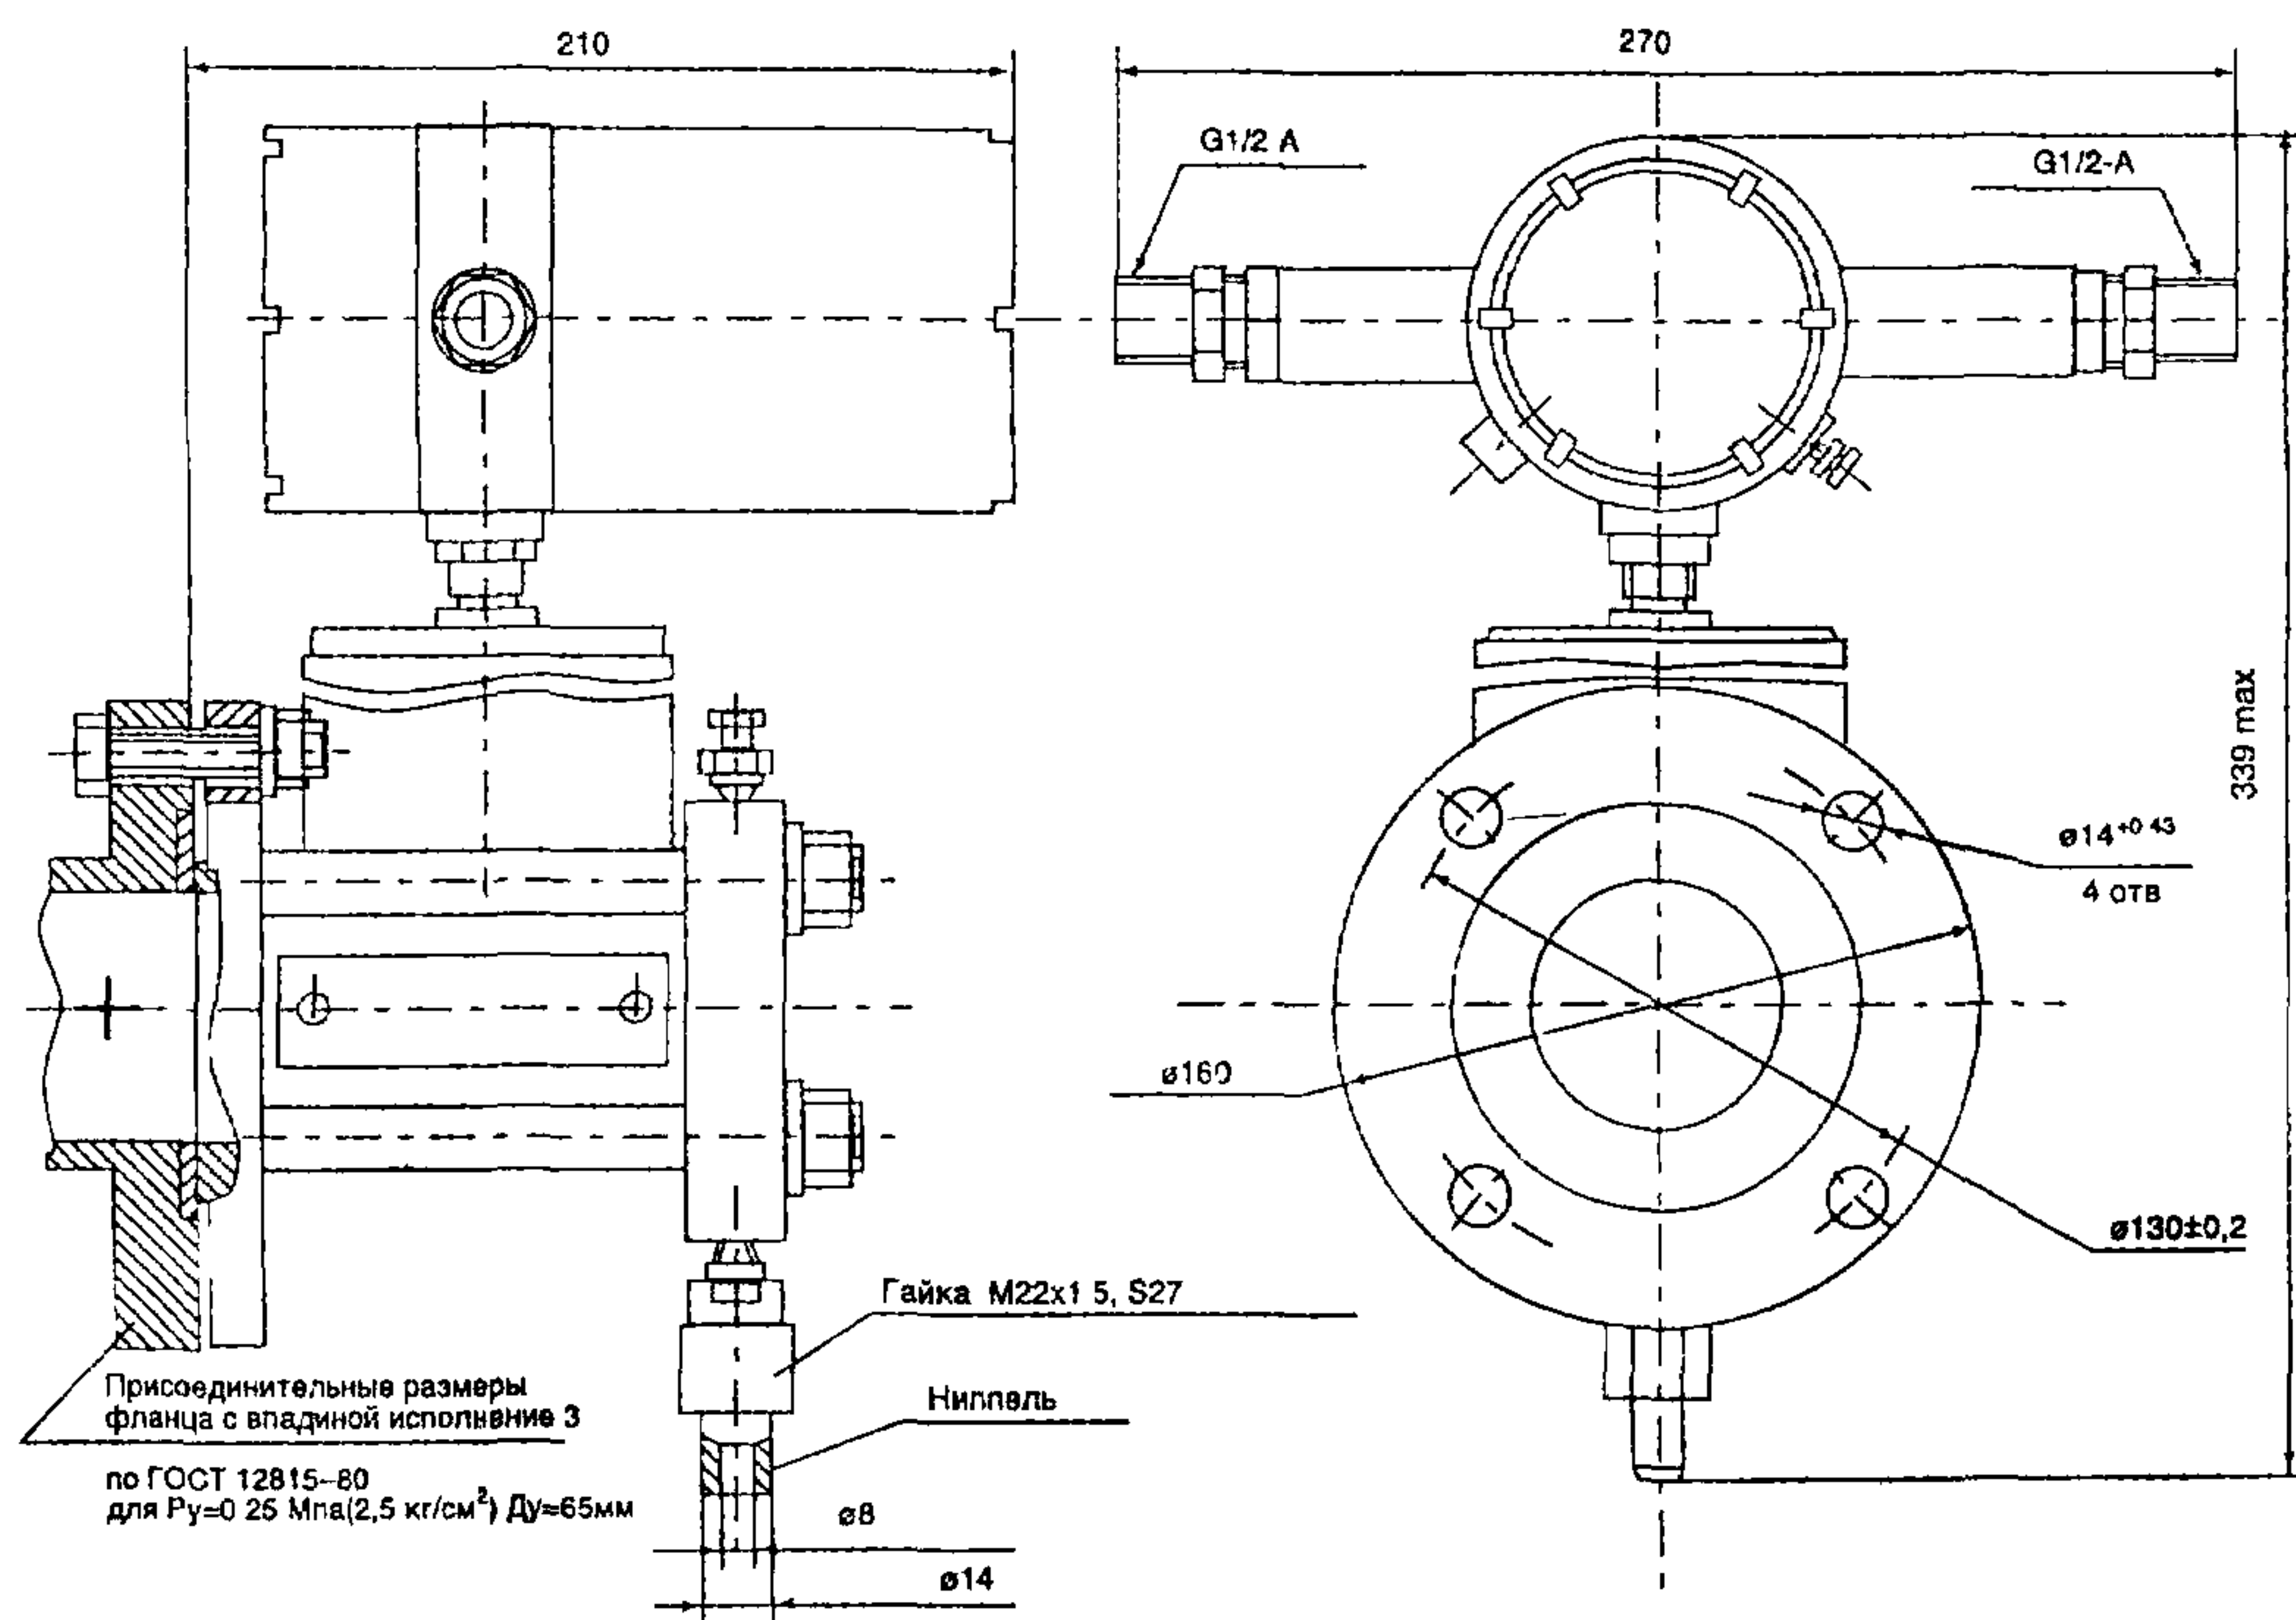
Габаритные, установочные и присоединительные размеры преобразователя Сапфир-22К-ДА-1
